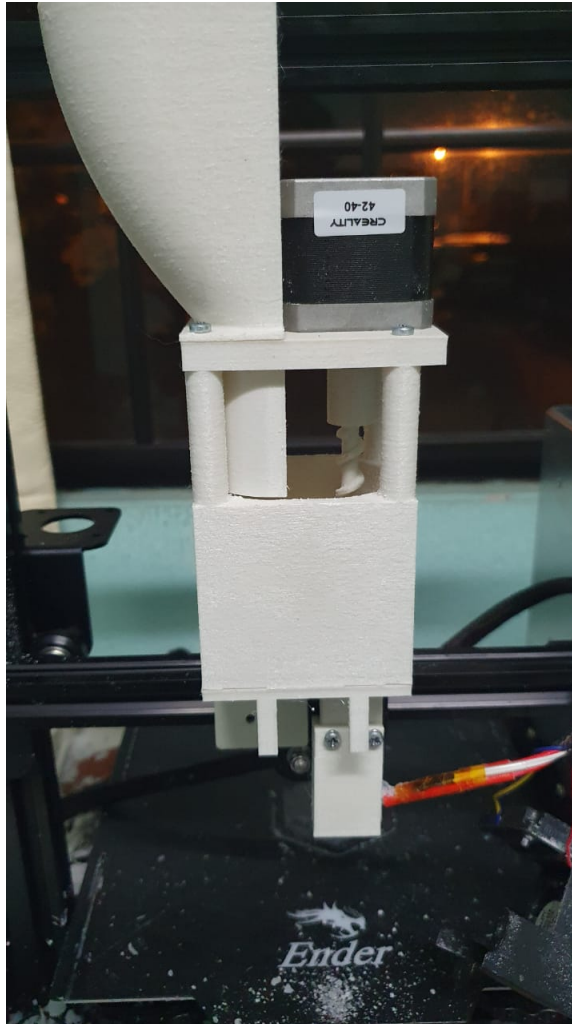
Colocar el bloque del motor a la parte superior de la placa
